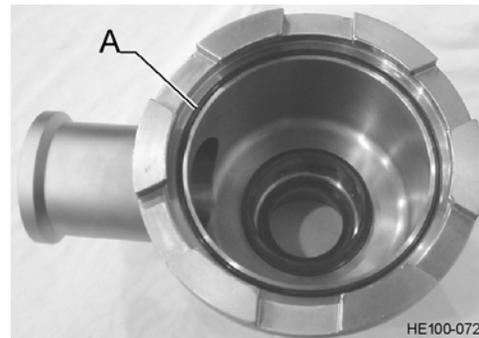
Junta tórica de la cabeza del extremo impulsor
